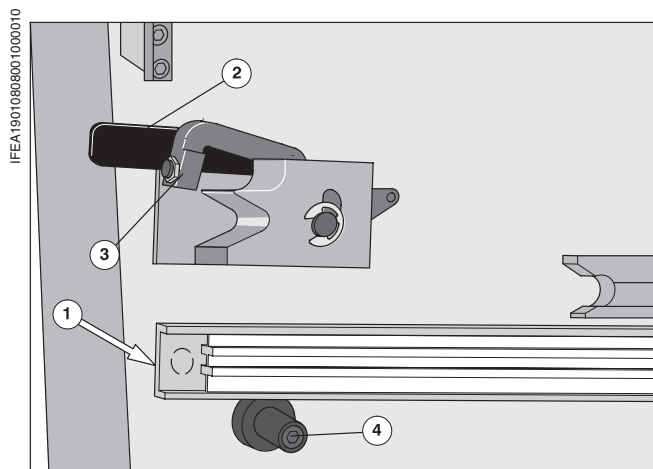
Направляющие рельсы и соединительная муфта для выдвижного блока нумератора
